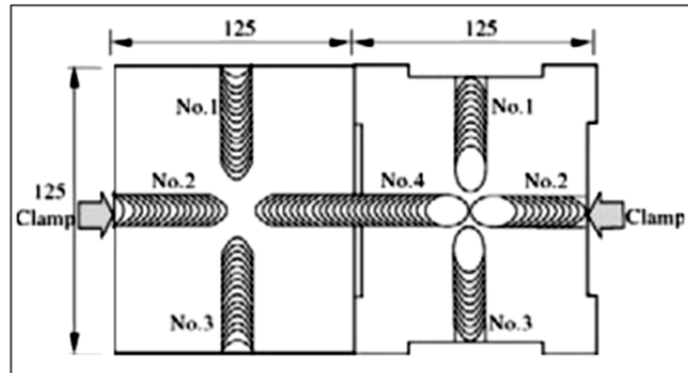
Éprouvette d'essai GBOP modifiée afin de pouvoir y déposer plusieurs soudures. Tirée de (Pitrun et Nolan, 2006)
